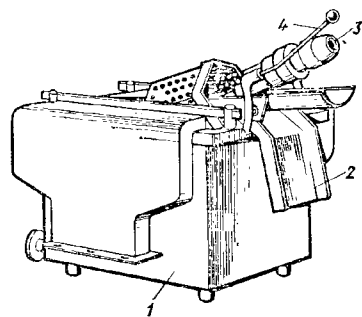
Колокольчатая ванна типа ВК-40; 1 — корпус ванны; 2 — лоток; 3 — электродвигатель для вращения колокола; 4 — ручка для подъема и опускания колокола
